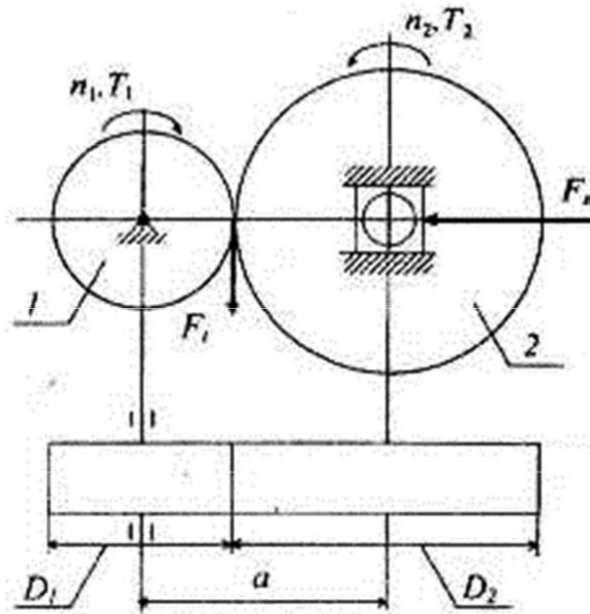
Схема циліндричної фрикційної передачі
